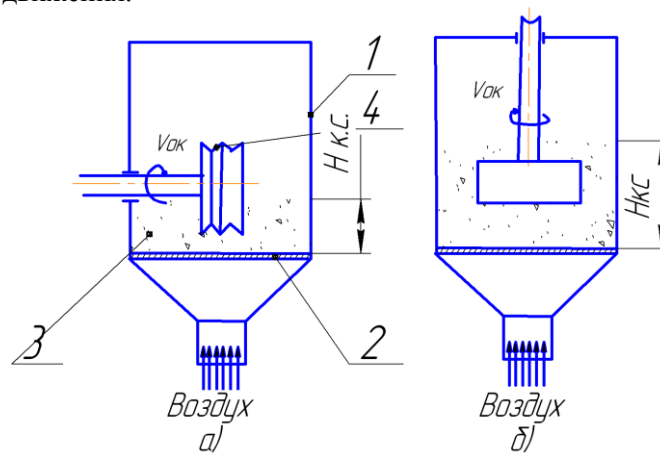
Схема процесса турбоабразивной обработки: а – с горизонтальной осью вращения заготовки; б – с вертикальной: 1 - рабочая камера; 2 - воздушнораспределительная решетка; 3 - абразивное зерно; 4 – заготовка
